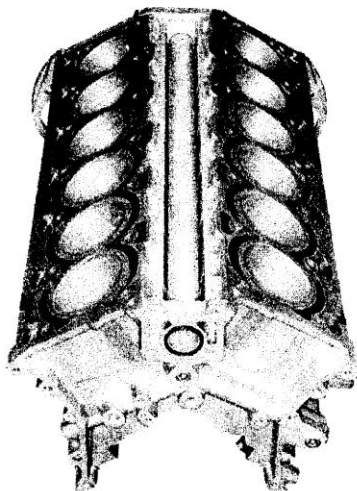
Блок цилиндров двигателя V12 фирмы BMW
